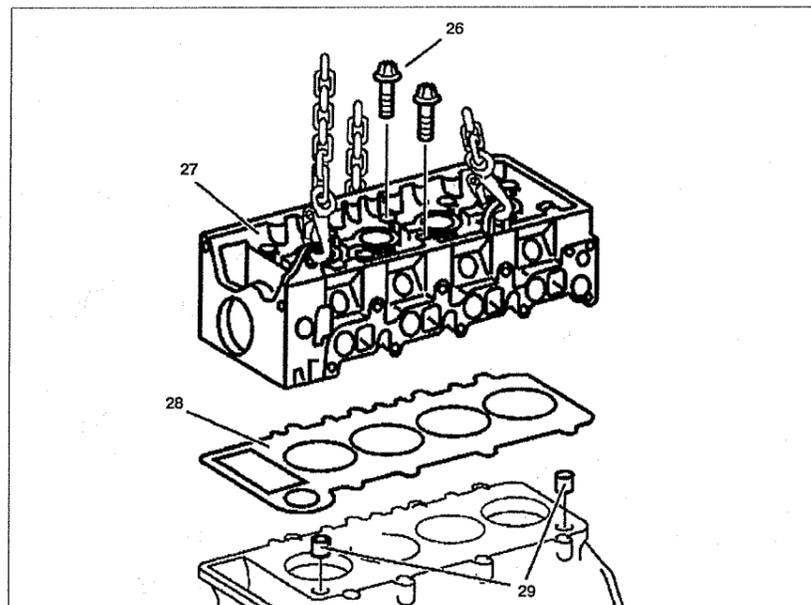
Головка блока цилиндров: 26. Болт крепления головки блока цилиндров, 27. Головка блока цилиндров, 28. Прокладка, 29. Направляющие пальцы.
